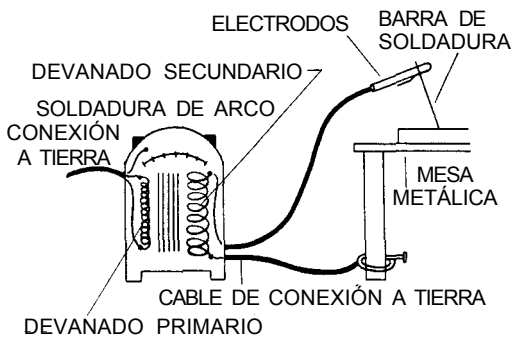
Soldadura por arco eléctrico.
